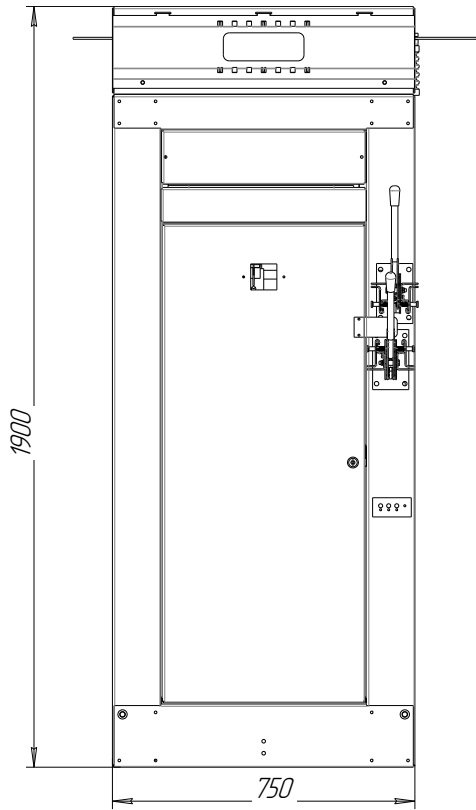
Габаритные размеры камеры КСО - 303 - 03
